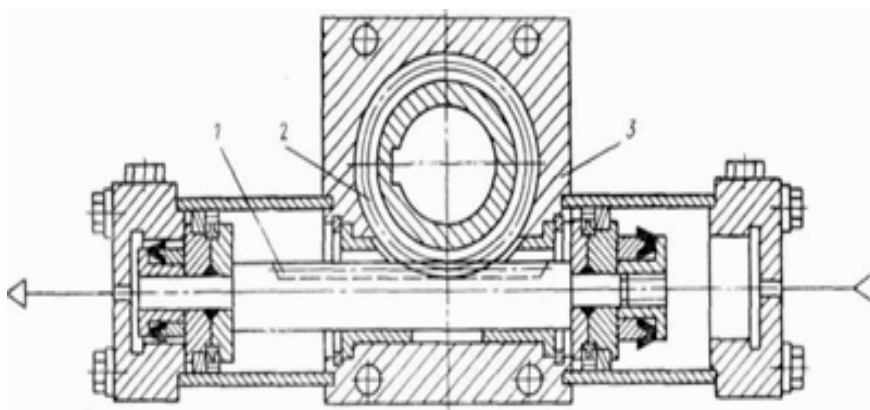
Двухпозиционный поворотный пневмодвигатель типа ПДП
